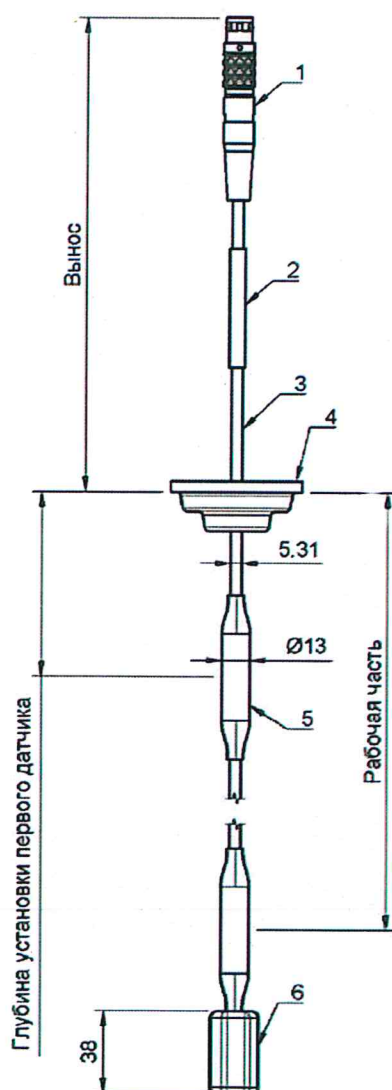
Габаритные размеры ИТМ2 и конструктивное исполнение,
